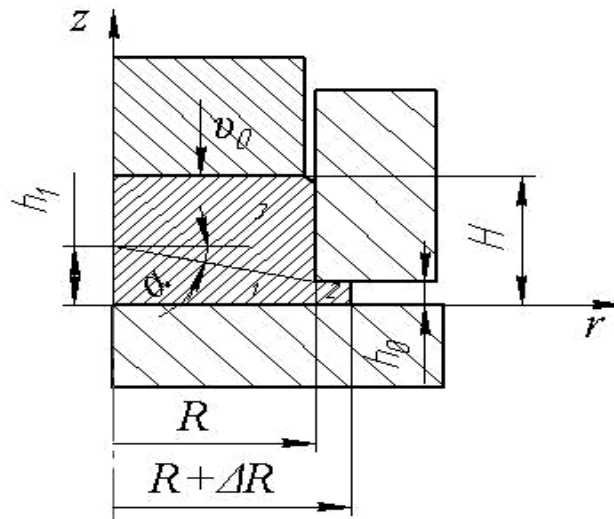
Розбивання низької заготовки на зони та визначення геометричних розмірів
